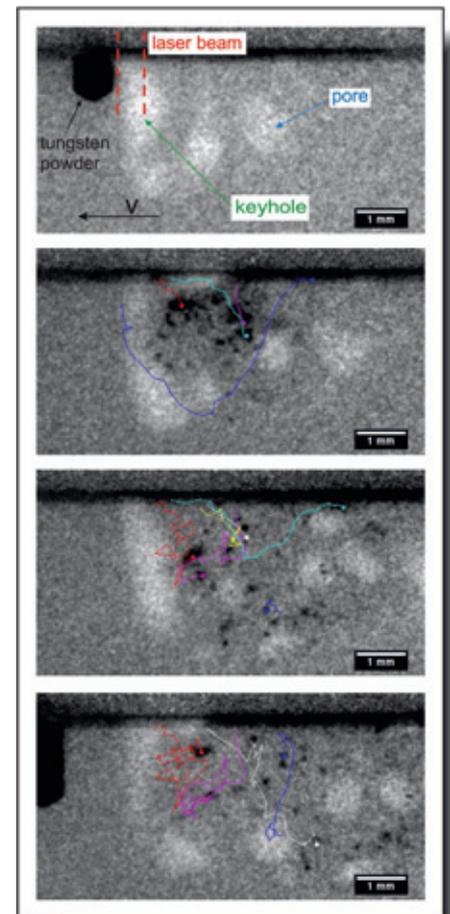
Schweißung in Aluminium. Als Tracer kommen Wolframpartikel zum Einsatz.
